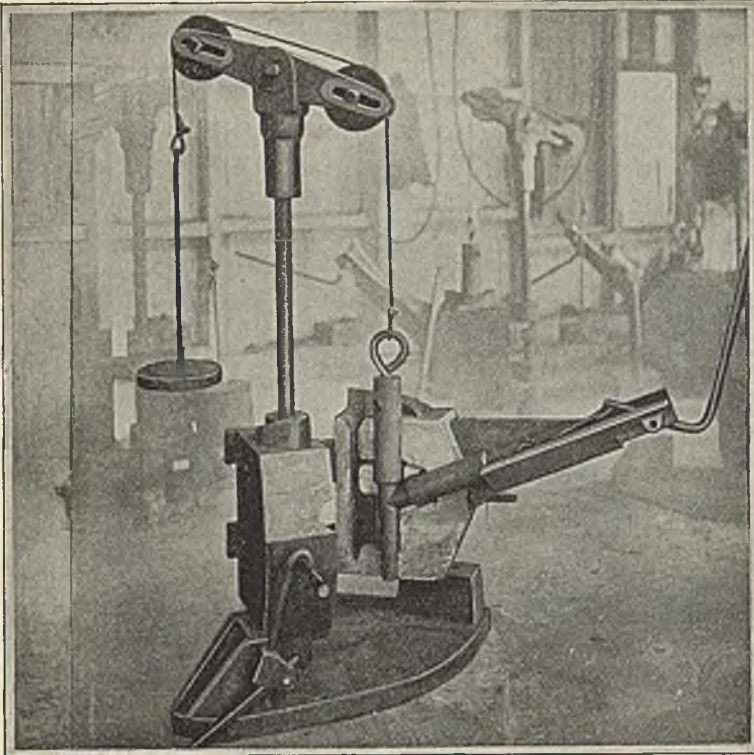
Formmaschine für schräge Abzweigstücke.
